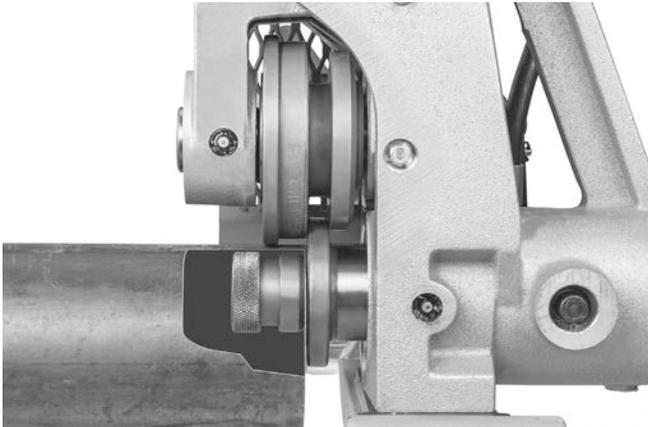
Размещение трубы на приводном валу, заподлицо с фланцем приводного вала (стабилизатор снят для ясности)
